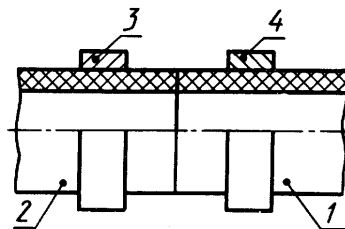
Схема сварки поперечного стыка труб ПВХ
